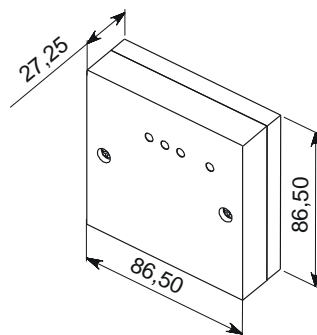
Внешний вид прибора в корпусе с габаритными размерами.
